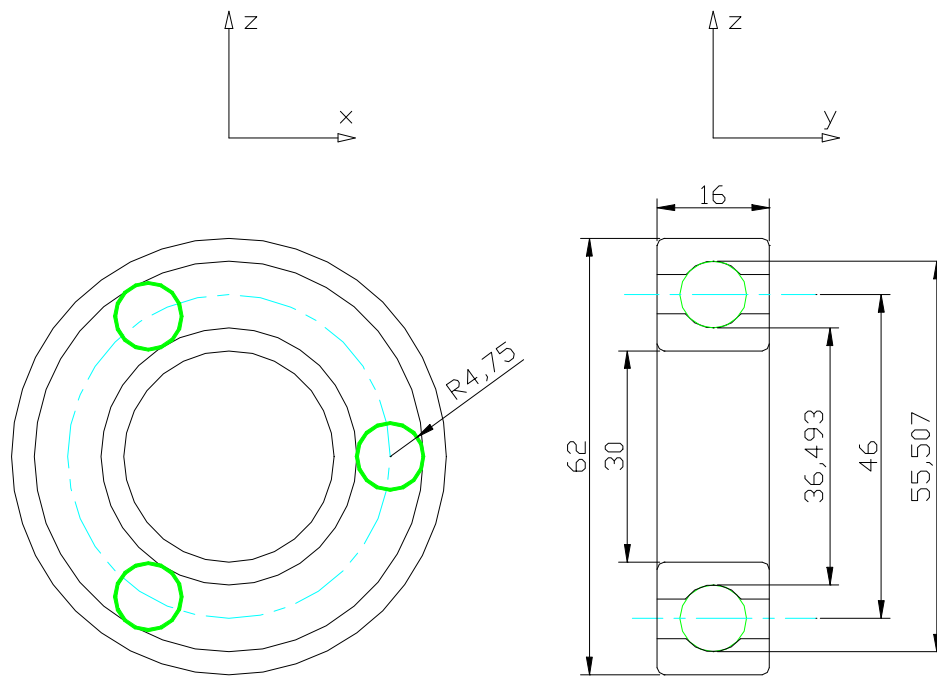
Dimensiones del rodamiento de bolas 6206
